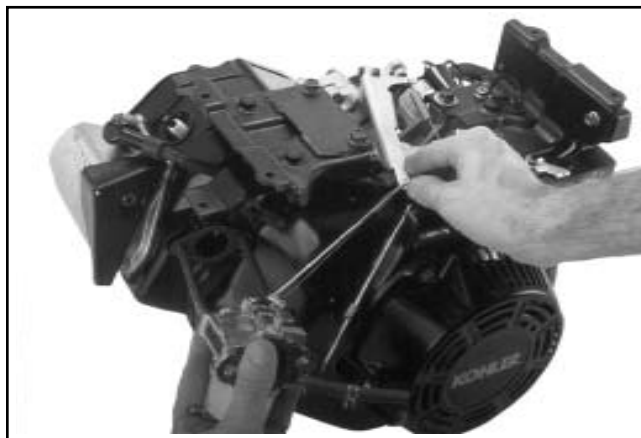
Rimozione del carburatore senza braccio del regolatore.
